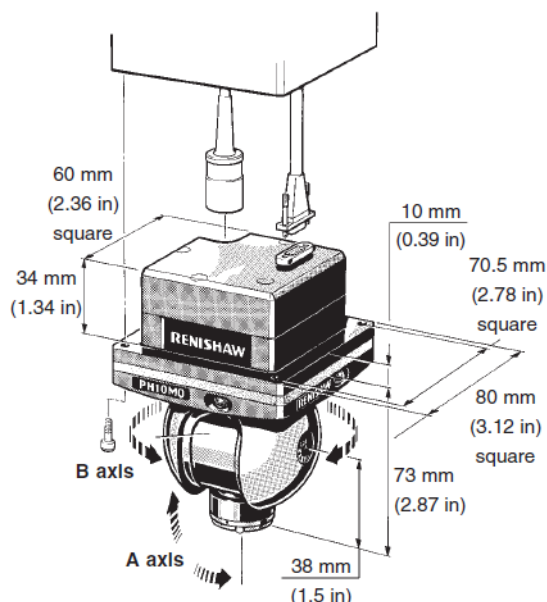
Поворотная головка Renishaw PH10MQ
